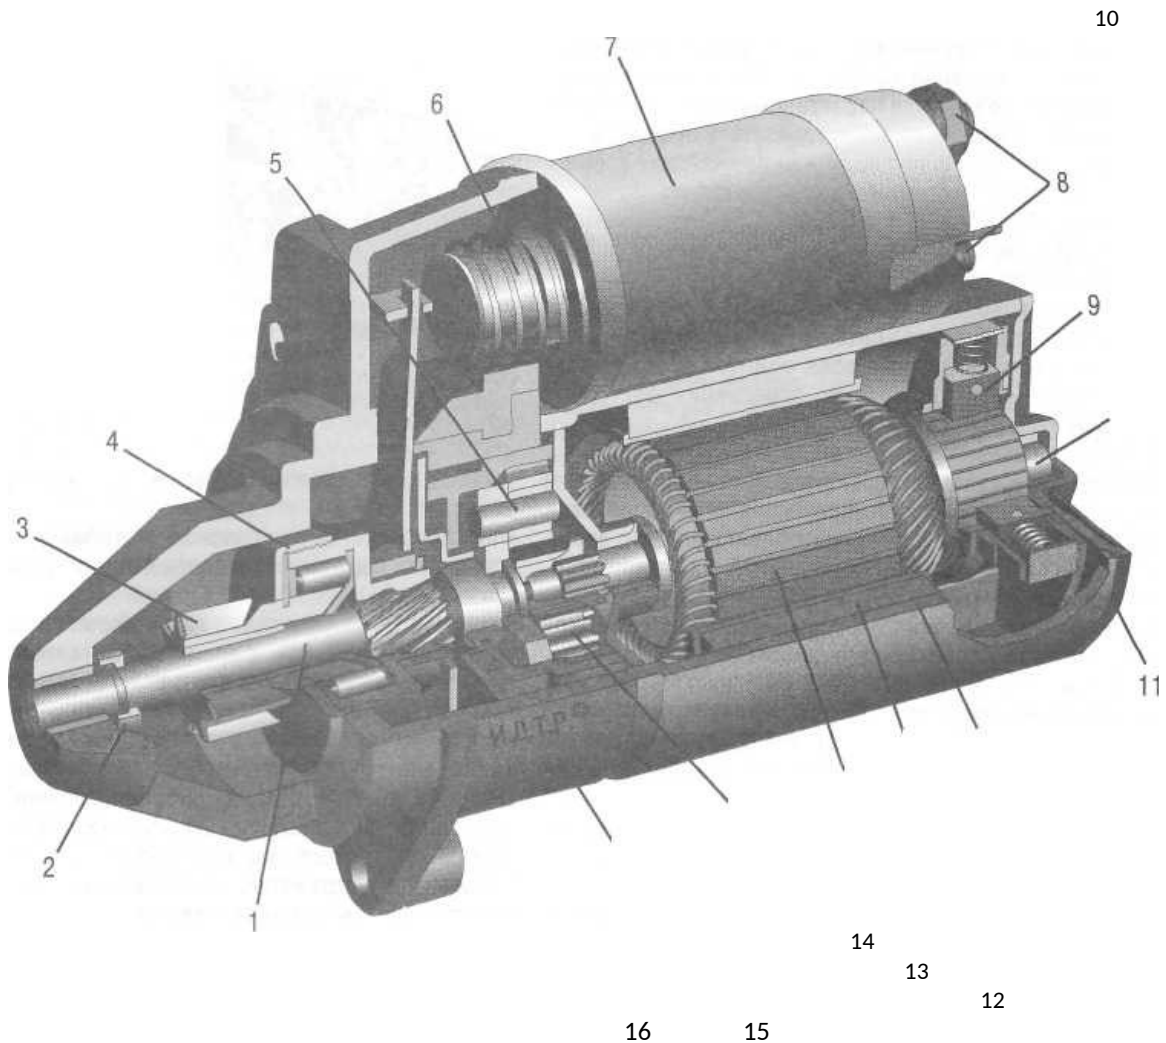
Устройство стартера: 1 - вал привода; 2 - ограничительное кольцо; 3 - шестерня с внутренним кольцом обгонной муфты; 4 - обгонная муфта; 5 - ось планетарной шестерни; 6 - якорь реле; 7 -тяговое реле; 8 - контактные болты; 9 - «положительная» щетка; 10 - вал якоря; 11 - кожух; 12 - корпус; 13 - постоянный магнит; 14 - якорь; 15 - планетарная шестерня; 16 - промежуточное кольцо.
